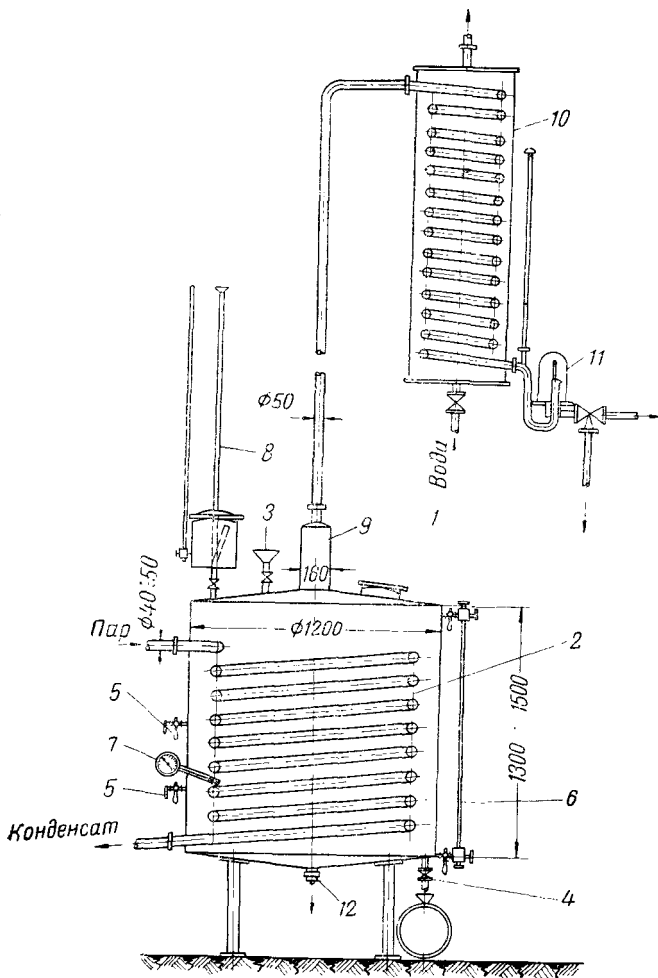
Установка для перегонки нестандартного сивушного масла:
